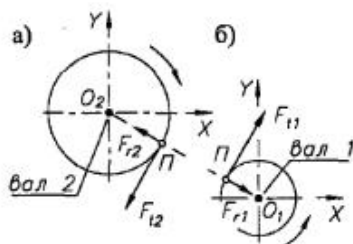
Схемы сил F_t и F_r , нагружающих валы: а) зубчатого колеса; б) шестерни
